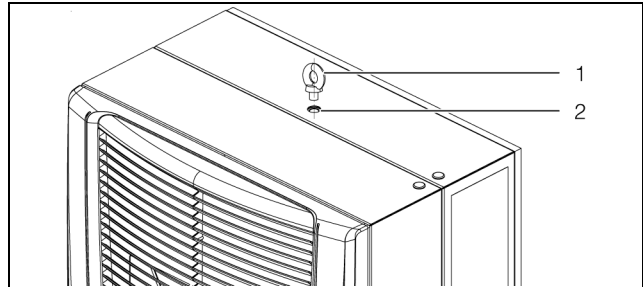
Отверстие и рым-болт в верхней части корпуса
